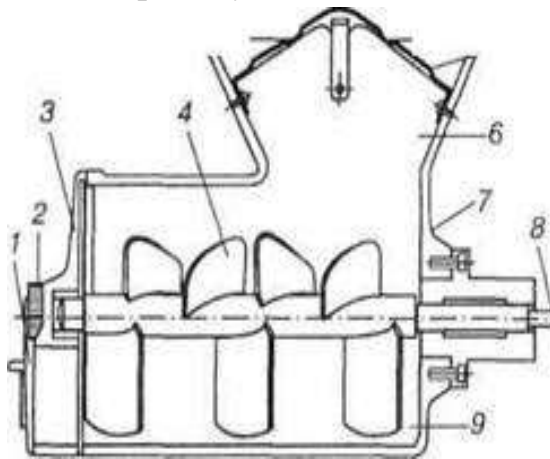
Механізм для перемішування фаршу МС8-150: 1 – заслінка; 2 – кришка; 3 – робоча камера; 4 – лопаті; 5 – запобіжна хрестовина; 6 – хвостовик
